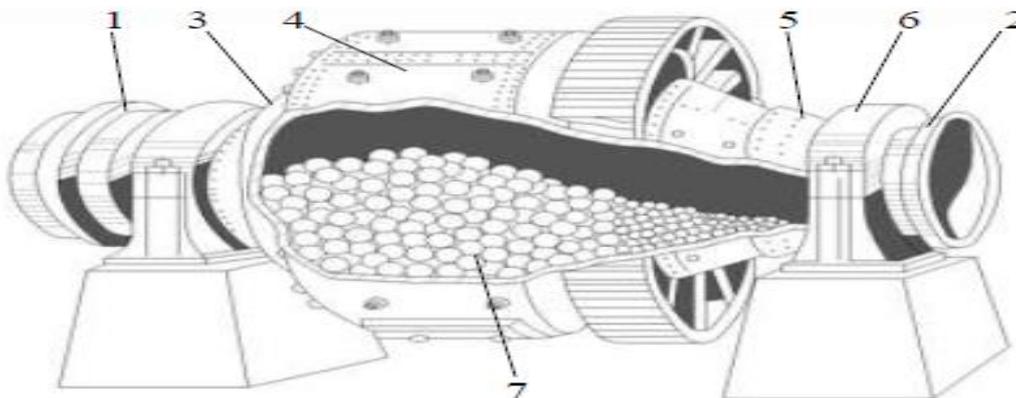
Шаровая мельница с комбинированной конструкцией корпуса:
